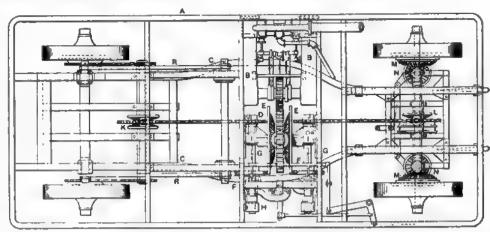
Aultman-Lastwagen: Grundriss.
